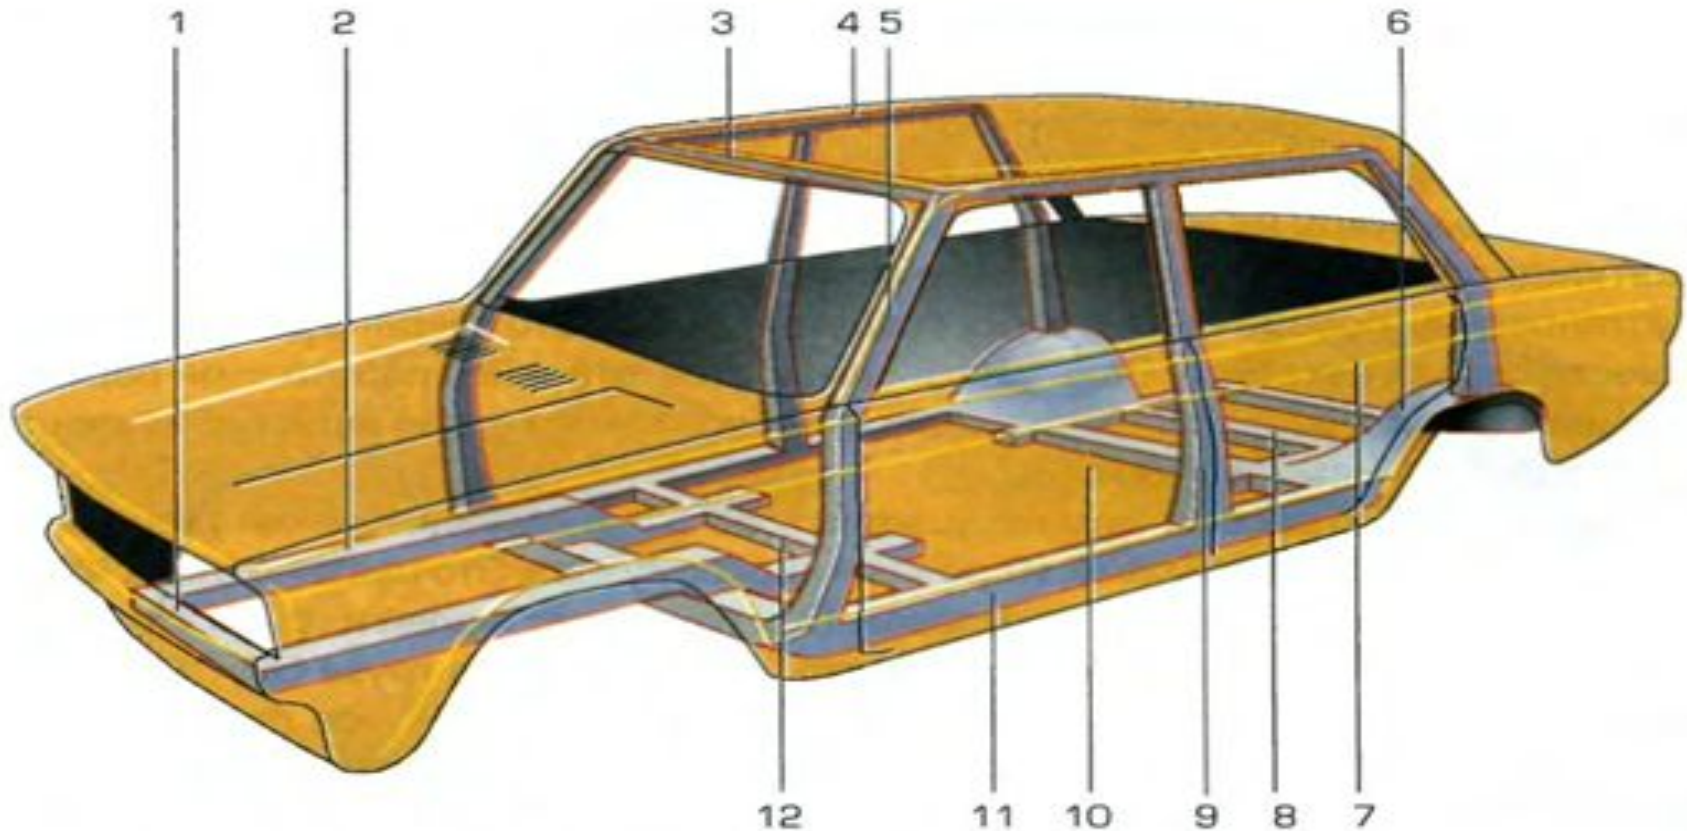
Схема несущего кузова легкового автомобиля: 1 – передняя силовая поперечина; 2 – передние лонжероны; 3 – панель крыши; 4 – усилители крыши; 5 – передняя стойка крыши; 6 – арки колес; 7 – задняя дверь; 8 – усилители пола багажника; 9 – стойки крыши; 10 – передняя дверь; 11 – пороги; 12 – усилители пола салона.
